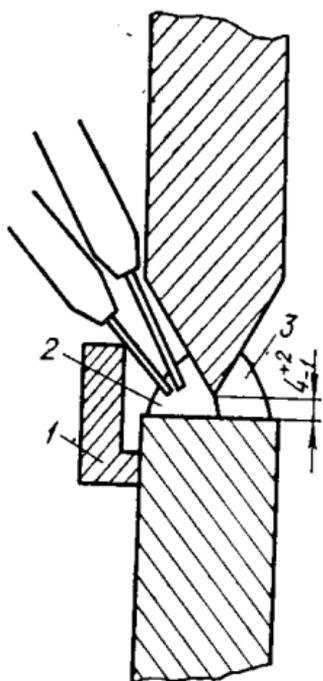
Схема сварки горизонтальных швов с полупринудительным формированием аппаратом А-1325:
